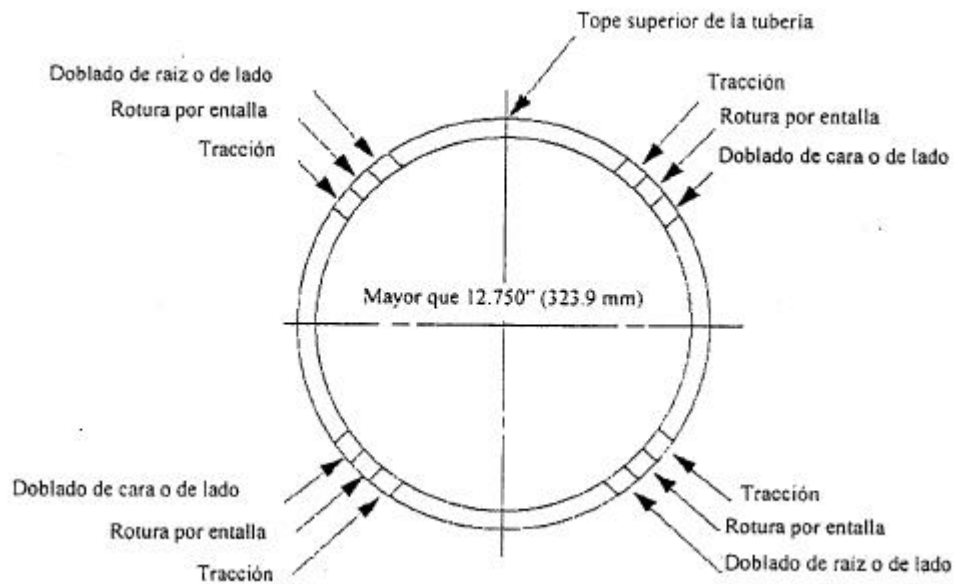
B: Ubicación de las probetas de ensayo de soldaduras a tope para ensayos de calificación de soldadores (diámetros mayor que 12.750" (323.9 mm))
